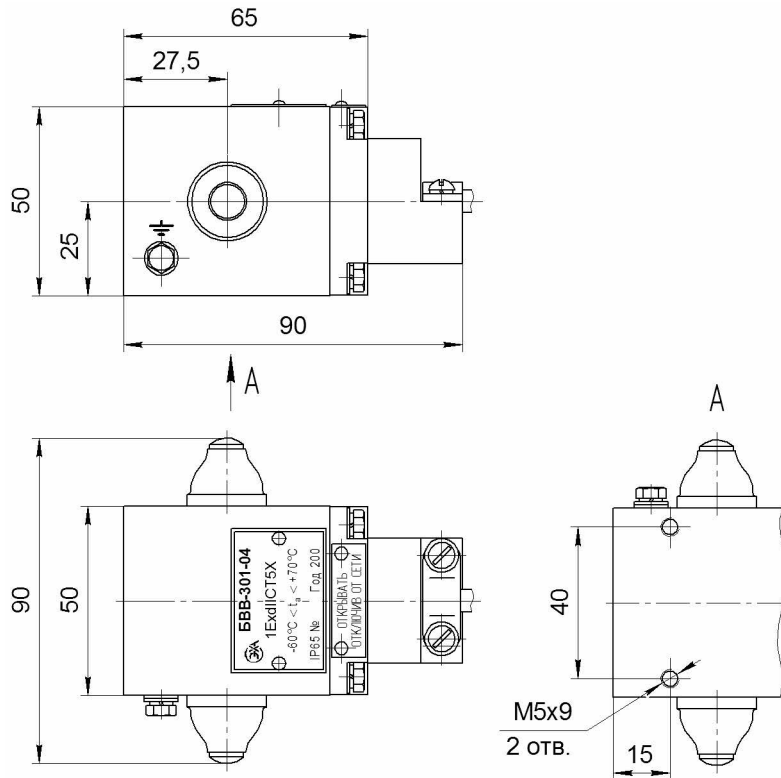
Габаритные и установочные размеры блока выключателей БВВ-301-04
